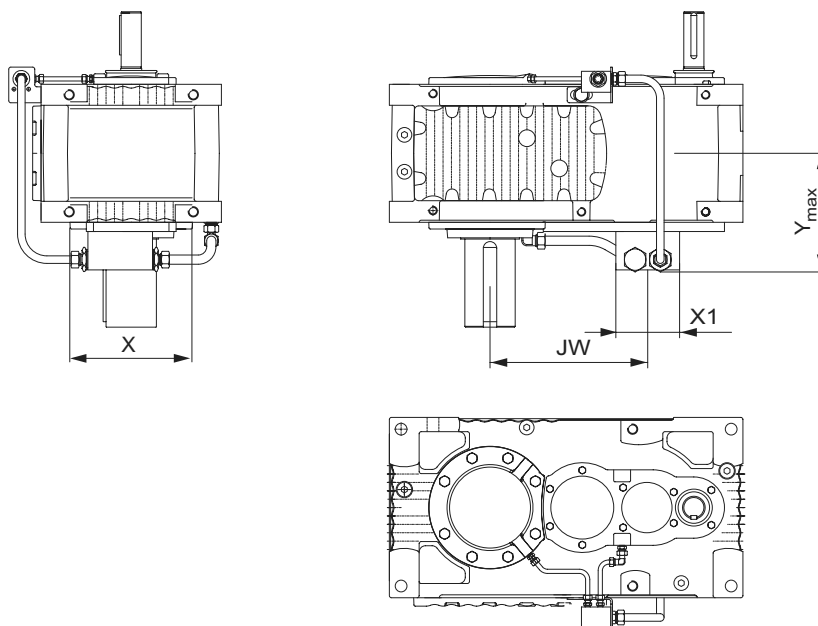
Dimensiones de montaje de MC3PV.. con bomba del extremo del eje 51845AXX
